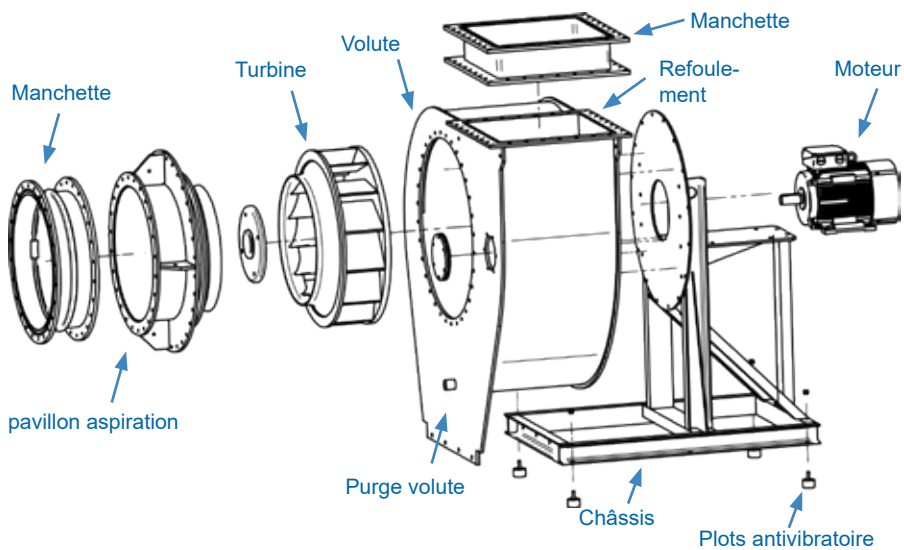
| Vue d'ensemble des ventilateurs HF R ...- 16 / 13 D | entraînement direct
